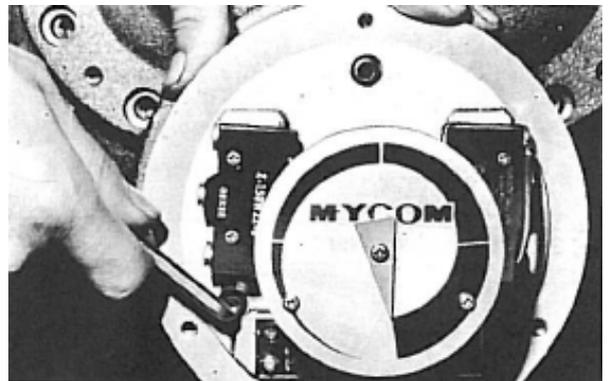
Dévissage des vis de la plaque support de micro-contact
